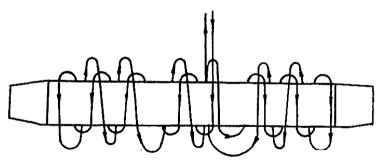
Схема намотки ДШ на корпус соединительного зажима.
